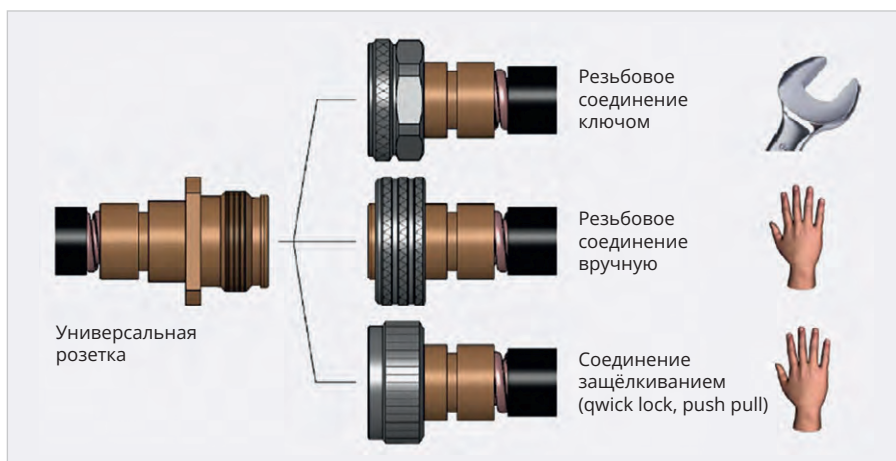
Соединители 4.3/10 с разными механизмами сочленения розетки и вилки
